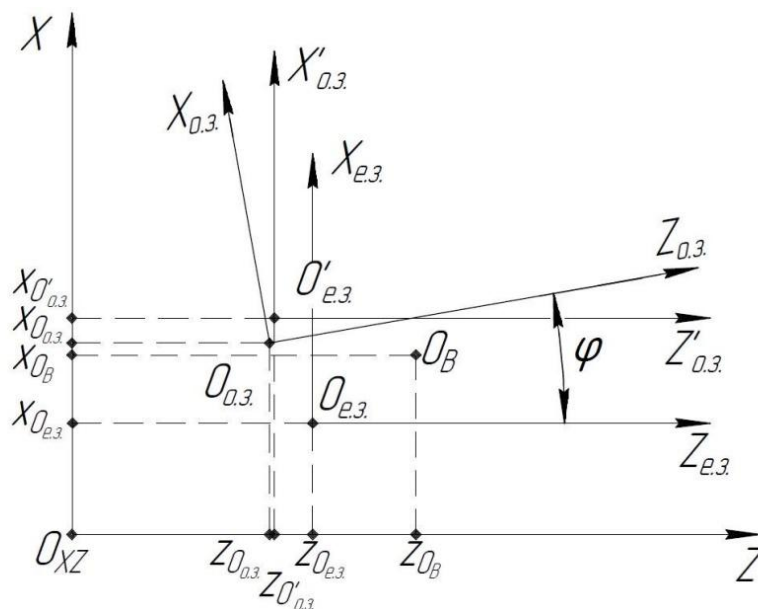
Схема відносного розташування осей систем координат верстата XZ, еталонної заготовки $X_{e.3}, Z_{e.3}$, оброблюваної заготовки $X_{o.3}, Z_{o.3}$, повернутої в робоче положення оброблюваної заготовки $X'_{o.3}, Z'_{o.3}$ та центру обертання обертового стола верстата O_B
